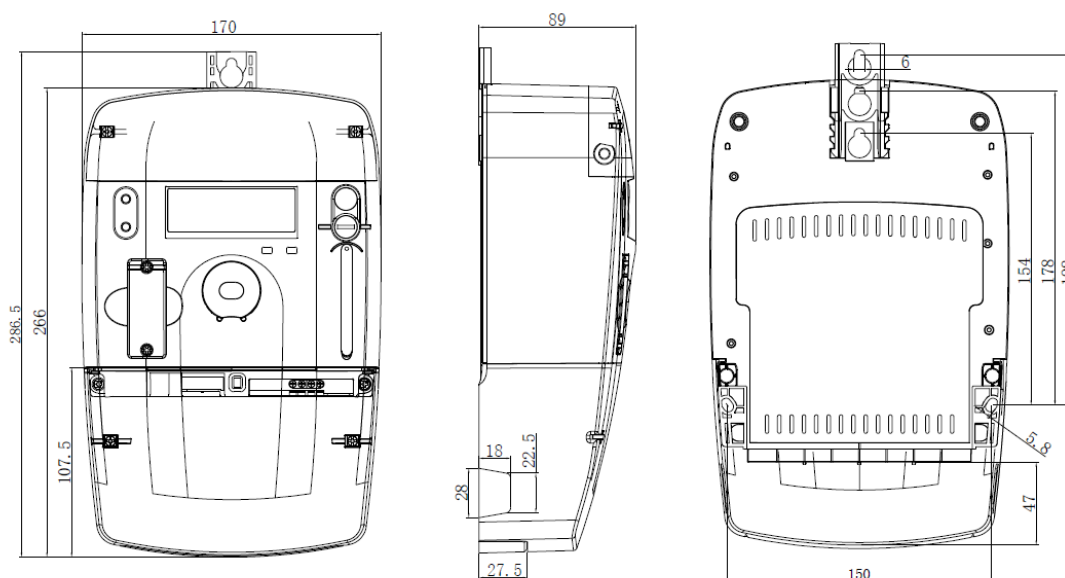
Габаритные и присоединительные размеры счетчика
